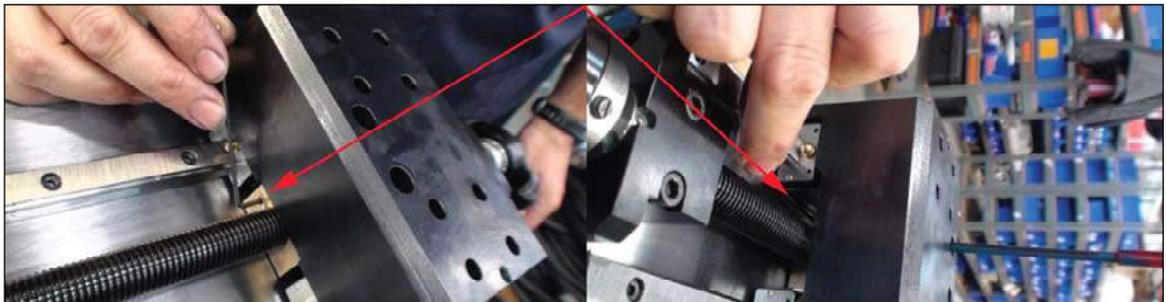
EMBLACEMENT DES VIS DE RÉGLAGE M4
